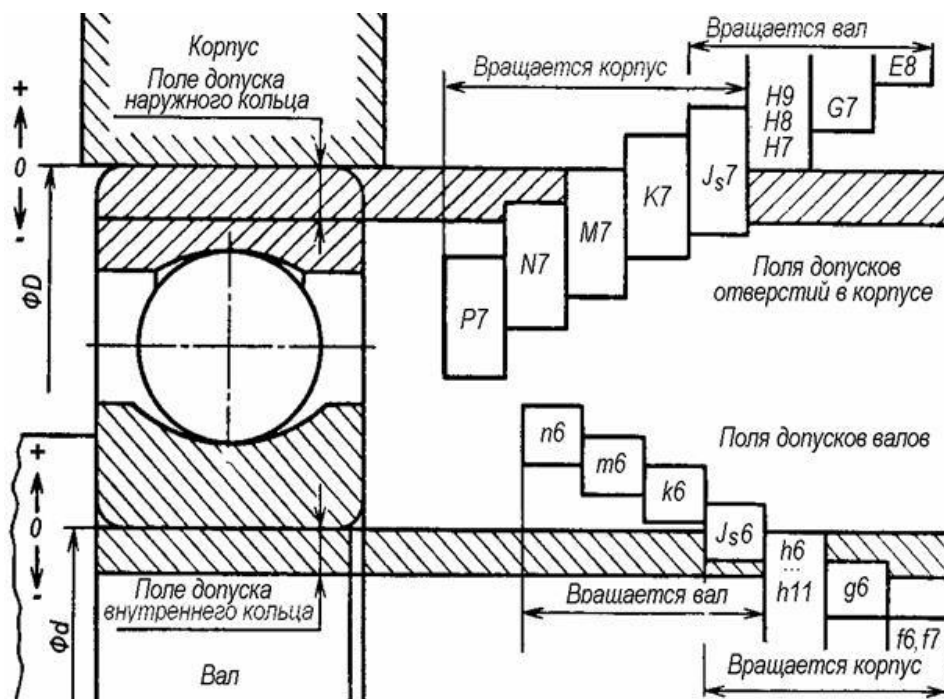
Поля допусков вала и корпуса при посадке подшипника
